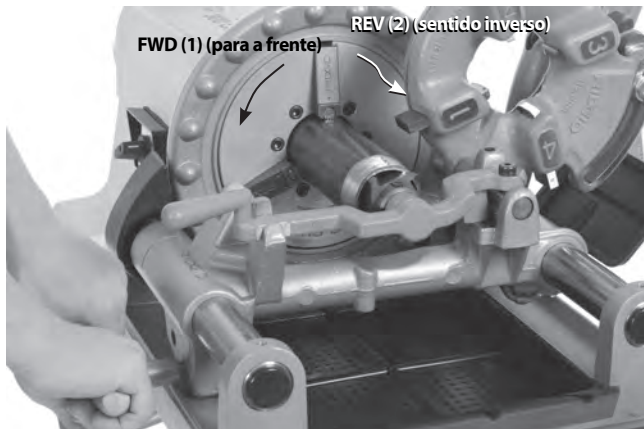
Brocagem do Tubo com um Escareador, Rotação da Máquina
